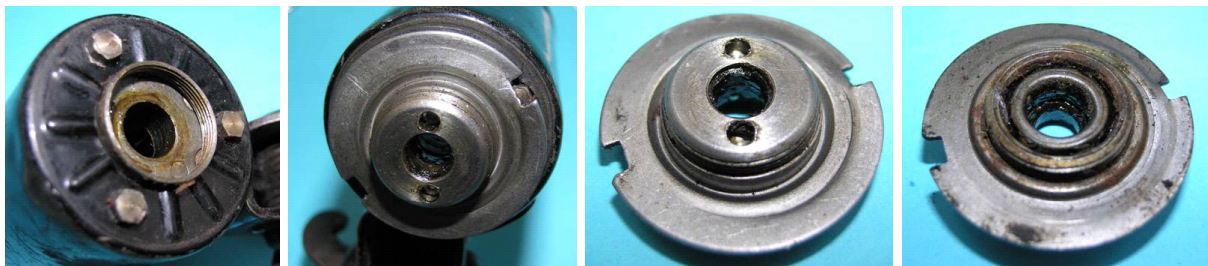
Lagerschale mit Außengewinde, b) Blechteller mit Innengewinde und äußerer Gewindebahn für die Schalterkappe
